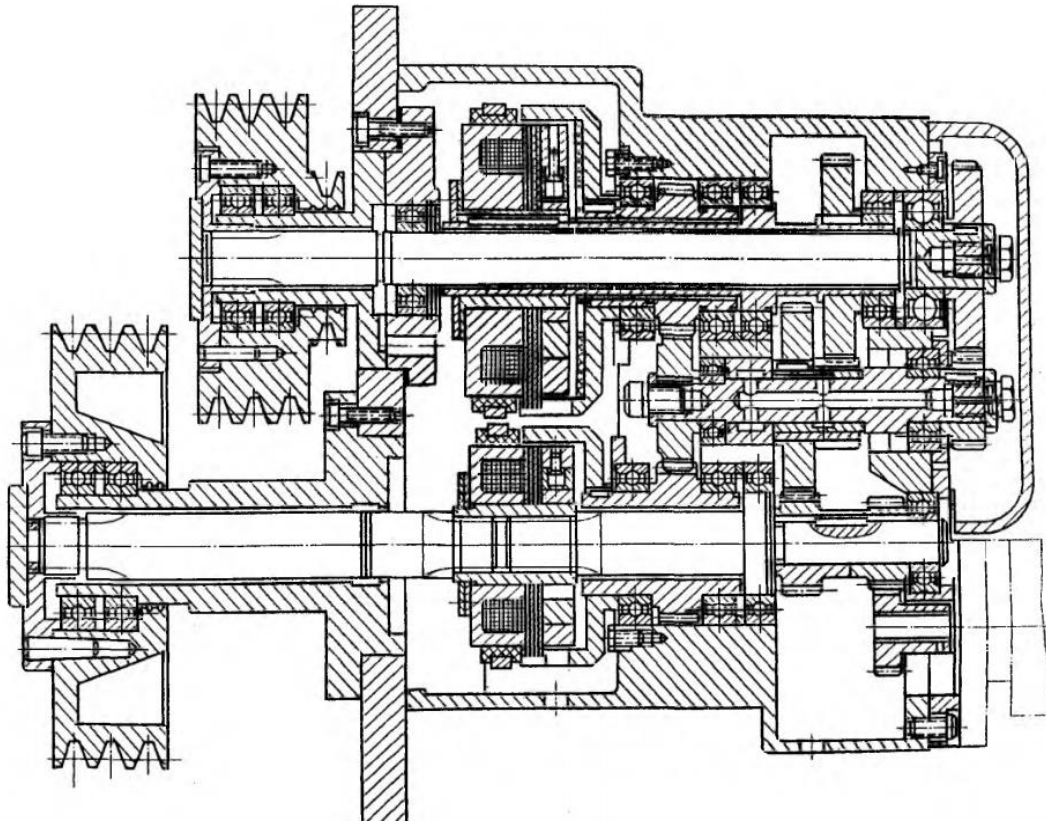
Редуктор приводу головного руху токарно-револьверного верстата.
